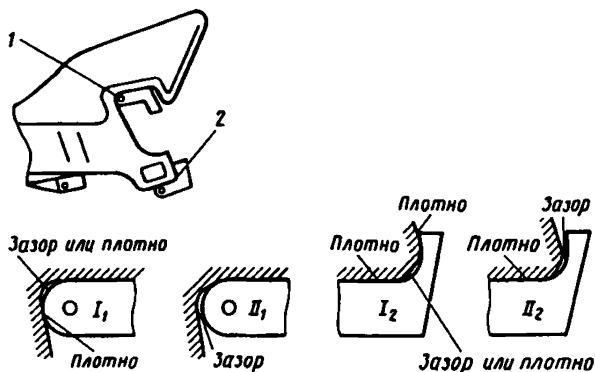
Проверка закруглений углов зева *1* и малого зуба *2* шаблоном 822р:
